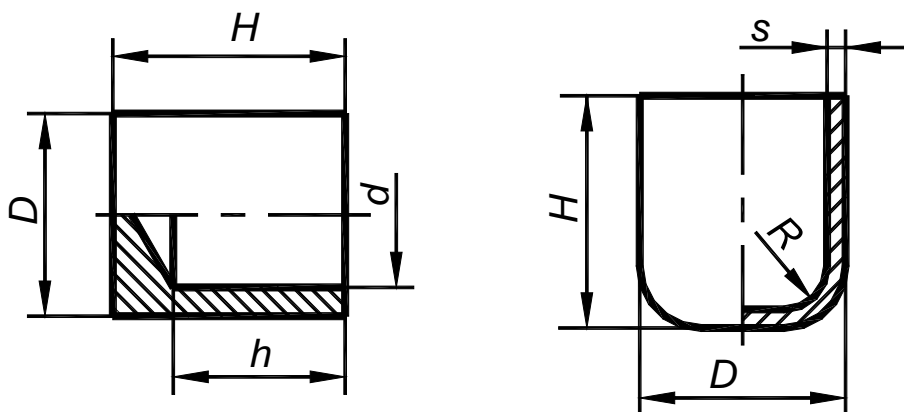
Детали цилиндрической формы с различной технологией изготовления
